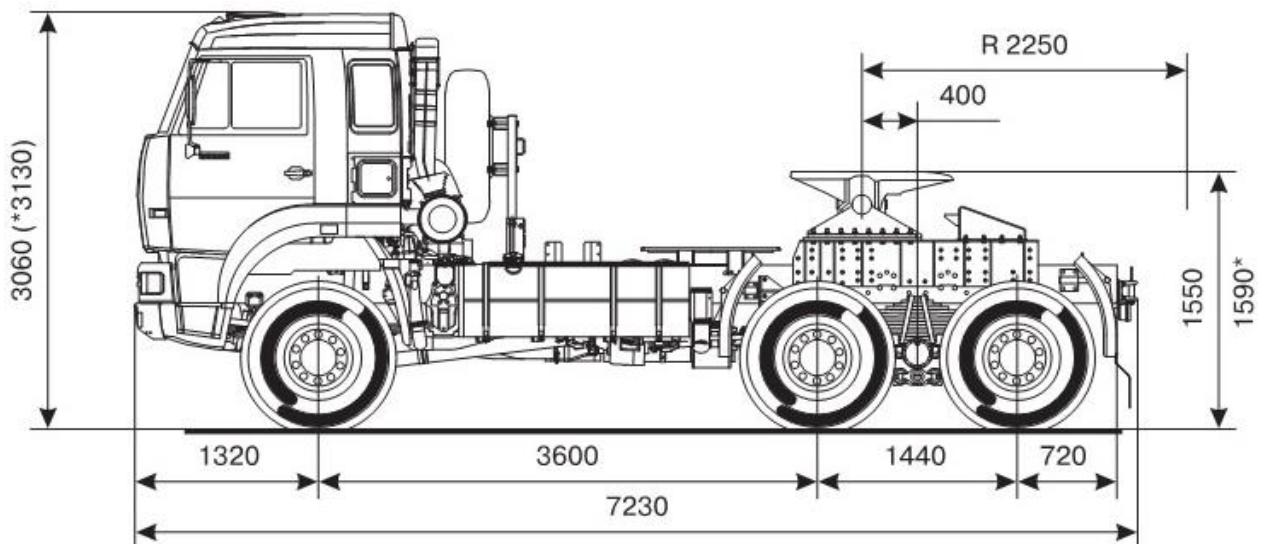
Габаритные размеры автомобиля КамАЗ-65225
